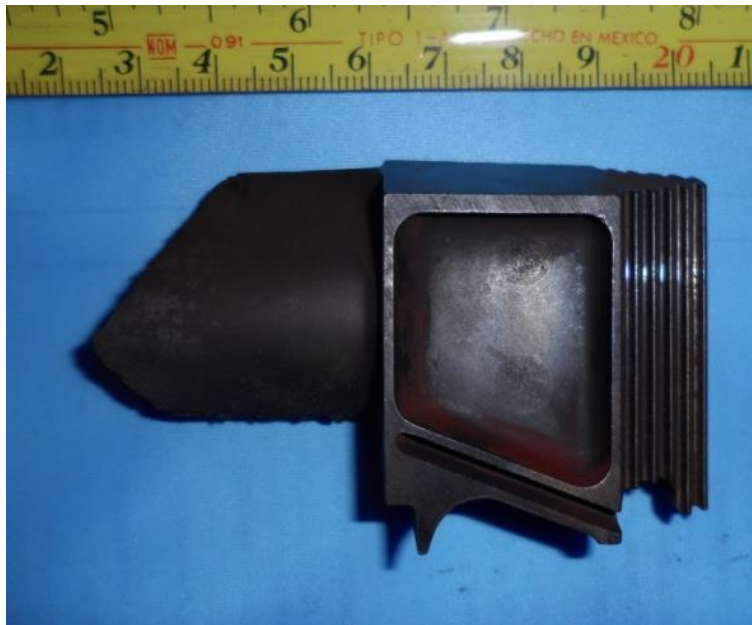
Álabe fracturado de material base Ni: Componente de una turbina de gas industrial
